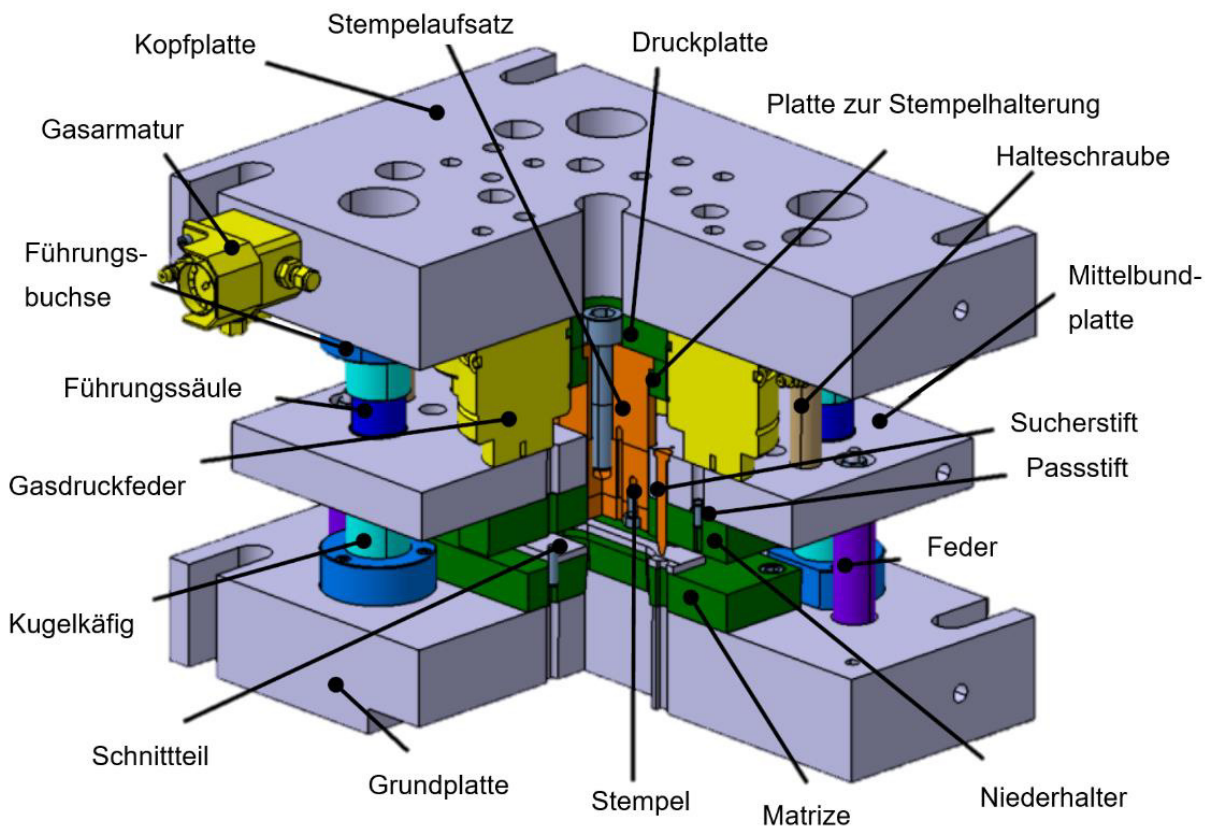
Schnitt durch das Zugproben-Scherschneidwerkzeug (Feistle et al., 2017)
